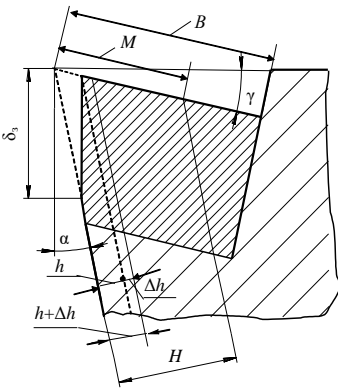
Схема переточування твердосплавного інструменту
